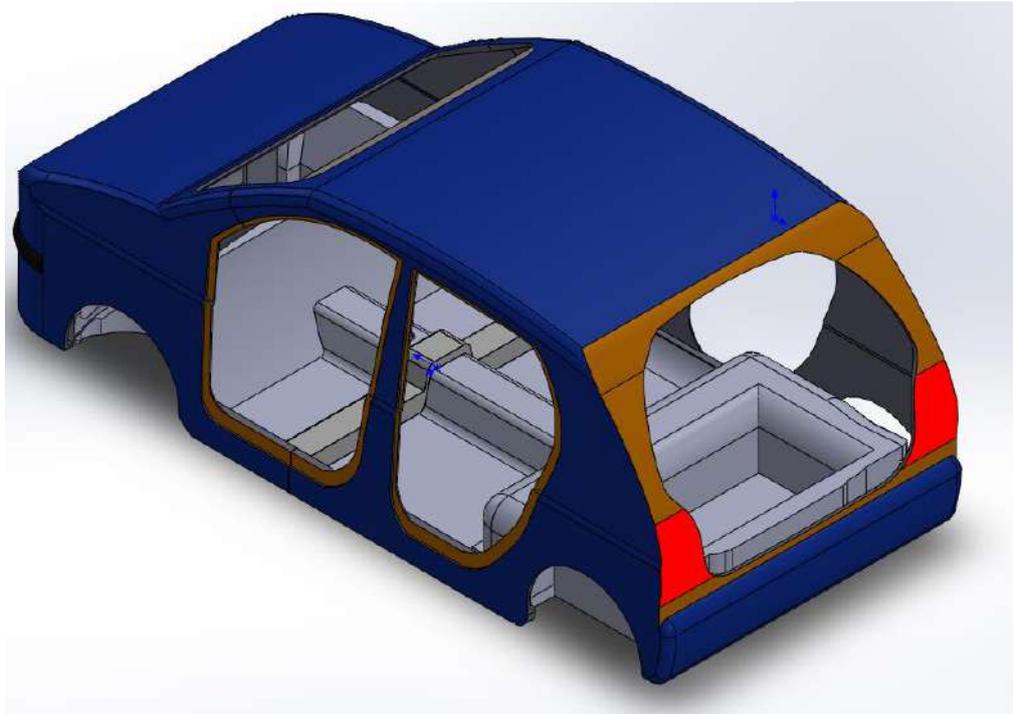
Diseño del ensamble de la carrocería vista isométrico
